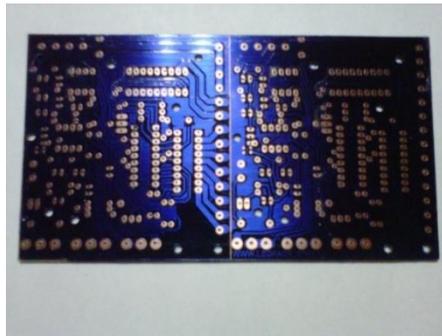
, 5 PCB realizada con la técnica del film fotosensible
